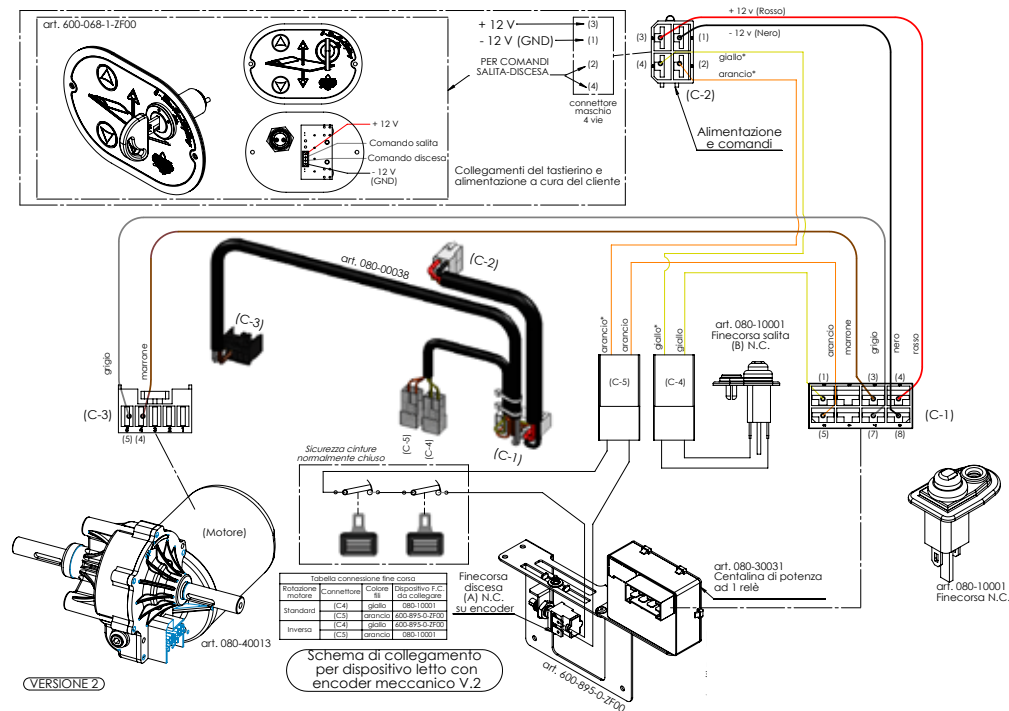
A – SCHEMA DEI COLLEGAMENTI
